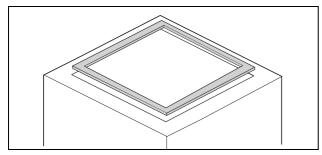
Cadre d'étanchéité sur le toit en tôle
